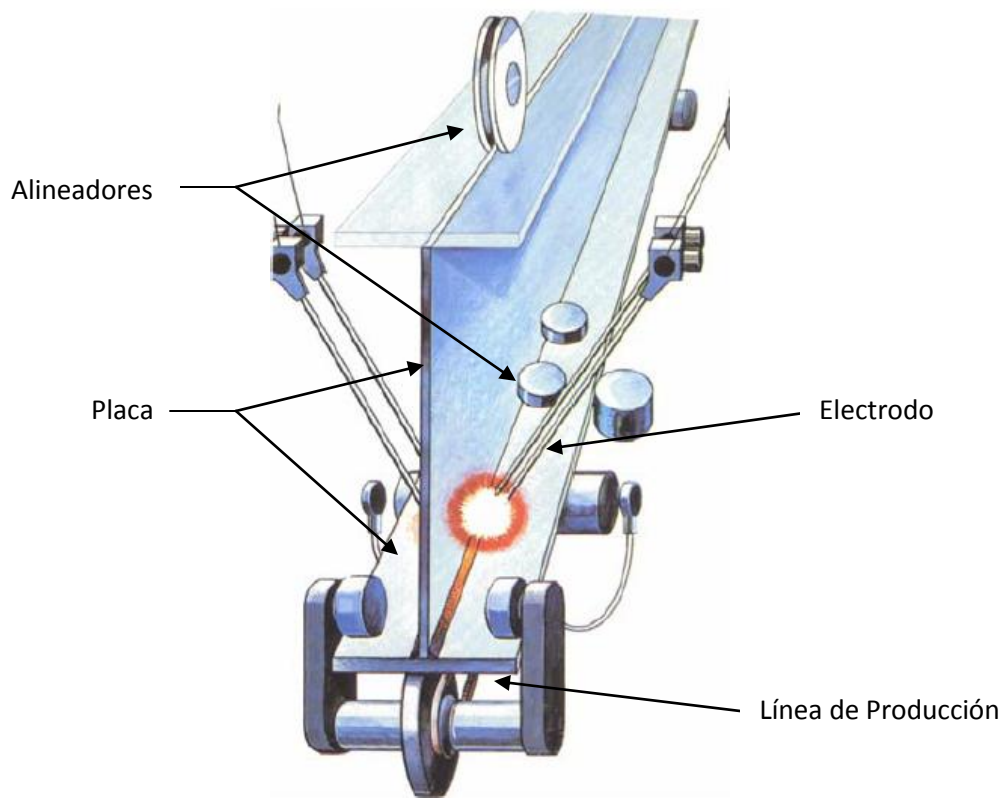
Aplicación de soldadura de arco eléctrico en taller
